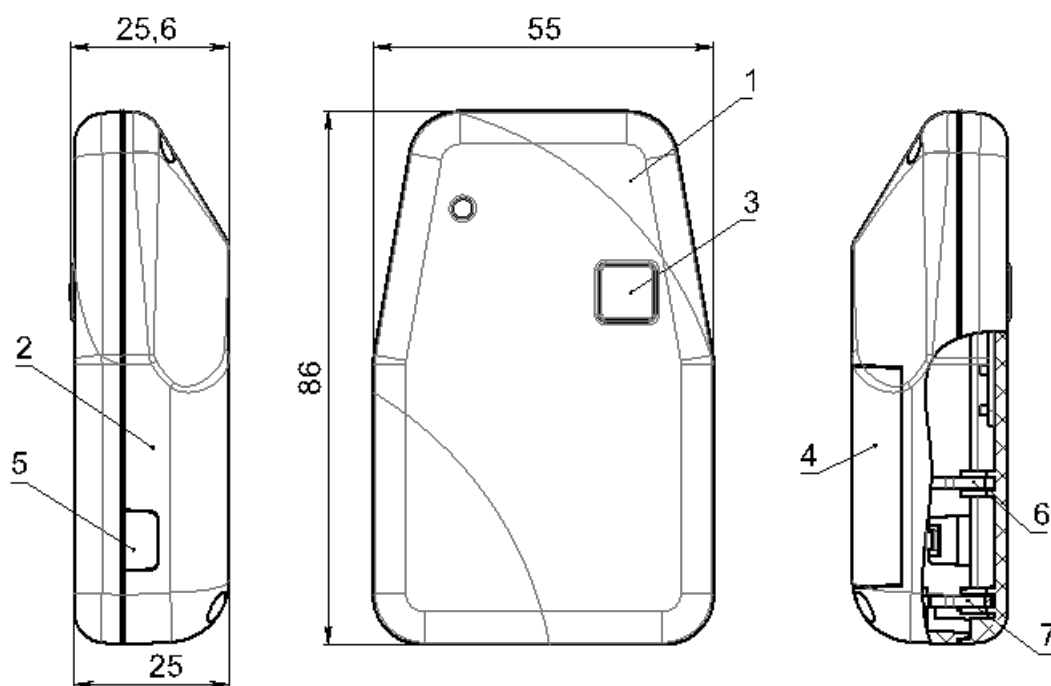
Сборочный чертёж корпуса прибора.
